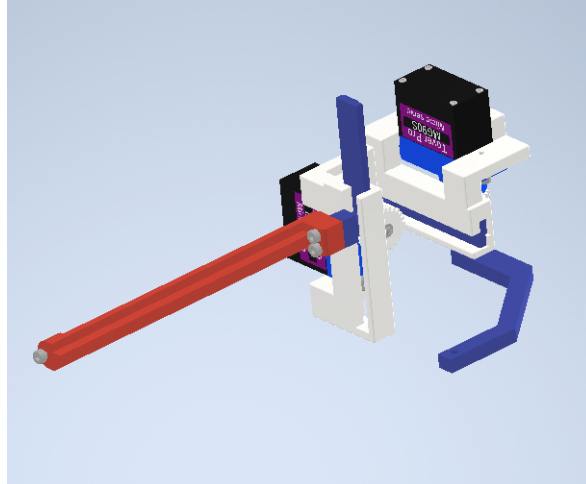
Sistema mecánico antiguo para ceja izquierda en CAD
